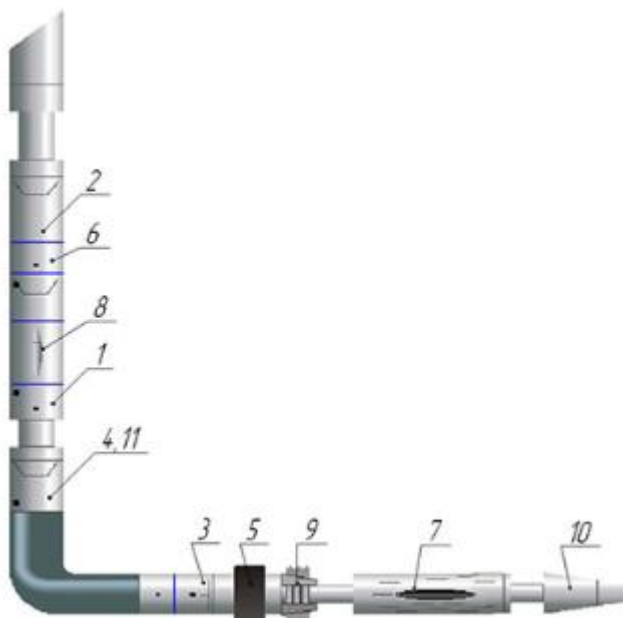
Пластоиспытательный комплекс ИПТ-80Г
